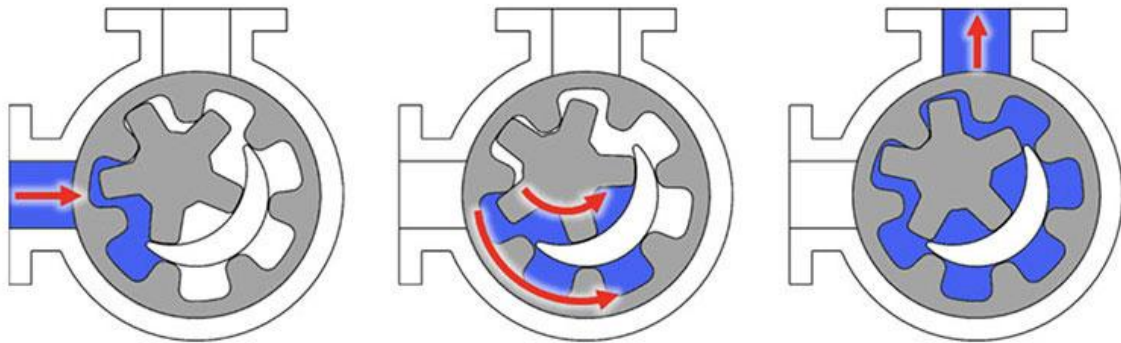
7 : Cycle de la pompe à engrenages internes.
